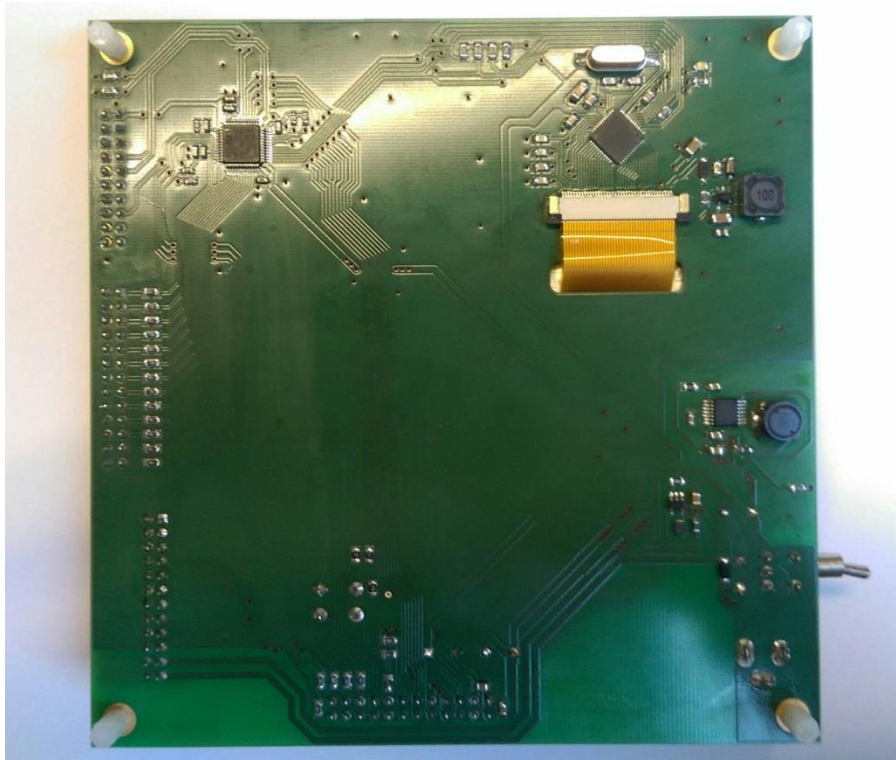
Hotová vývojová deska vysílače – pohled shora
